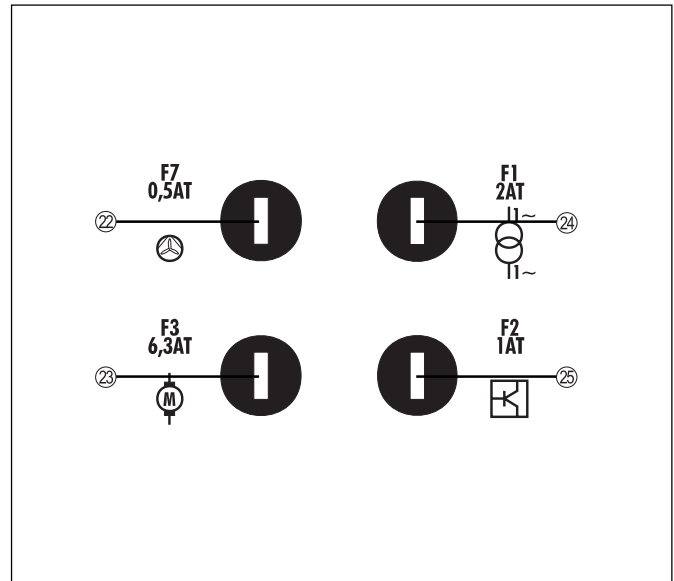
Sicherungen an der Innenseite des Schweißgerätes
